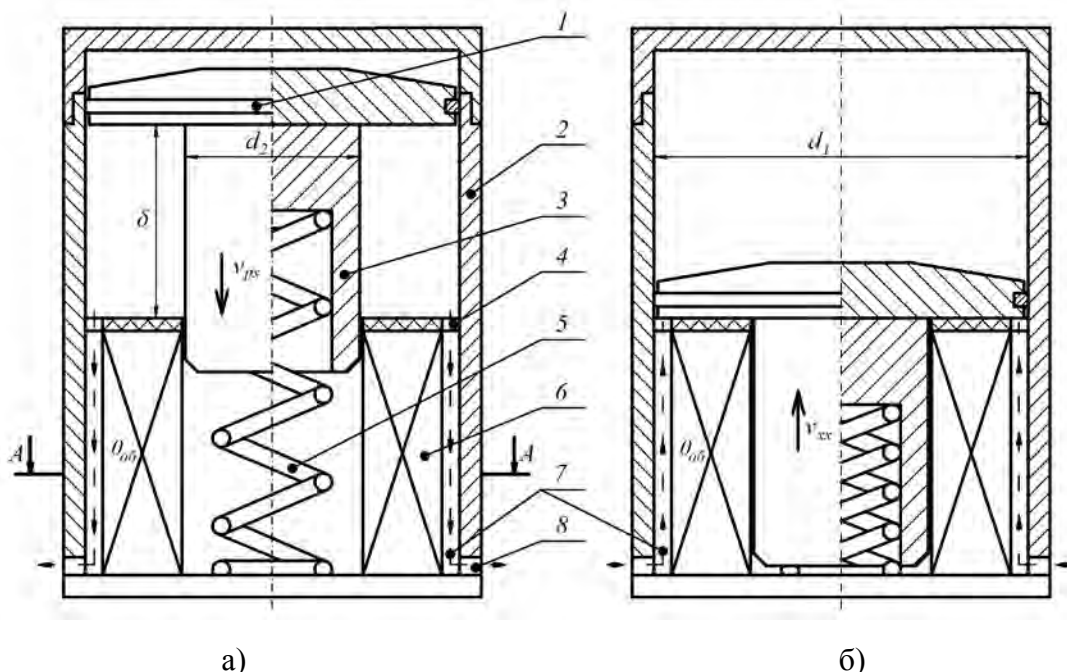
Конструктивные схемы ЛЭМД с самовентиляцией:
